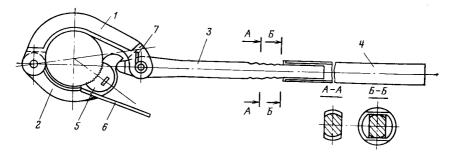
Трубный ключ КТД-114: 1— челюсть большая; 2— челюсть малая; 3— рукоятка; 4— удлинитель; 5— сухарь; 6— вспомогательная ручка; 7— пружина
